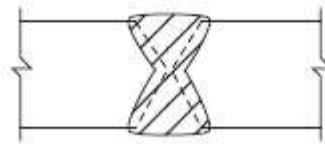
Soldadura a tope doblemente soldada.
